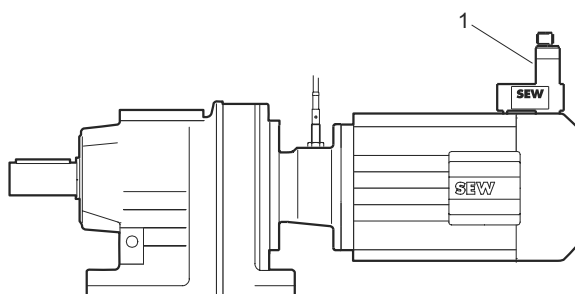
Motor regulado por rotação com tacômetro NV1 51659AXX
